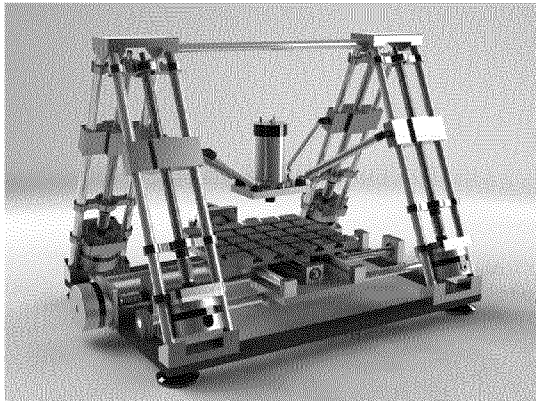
Настільний свердильно-фрезерний верстат клиновидної каркасної компоновки з МПС (КПІ)
